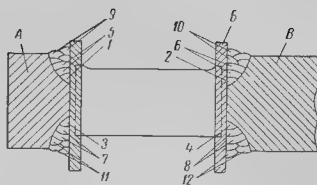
Схема сварки решетки с телом и ободом:
